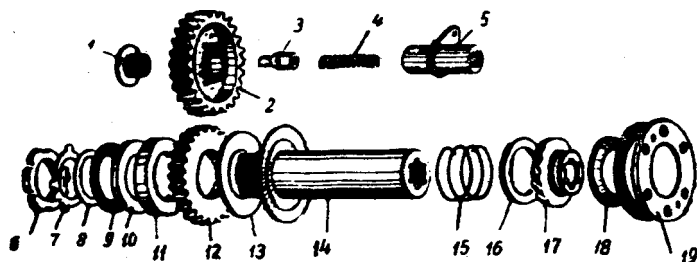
Детали привода генератора: 1—пробка оси; 2—промежуточная шестерня; 3, 7—замок; 4—пружина замка; 5—ось промежуточной шестерни; 6—гайка; 8—шайба; 9—пружинная шайба; 10—стальной диск; 11—бронзовое кольцо; 12—шестерня привода; 13—бронзовый диск; 14—валик; 15—пружина; 16—опорное кольцо пружины; 17—упорное кольцо с маслоотражателем; 18—уплотнительное кольцо; 19—упорное кольцо
